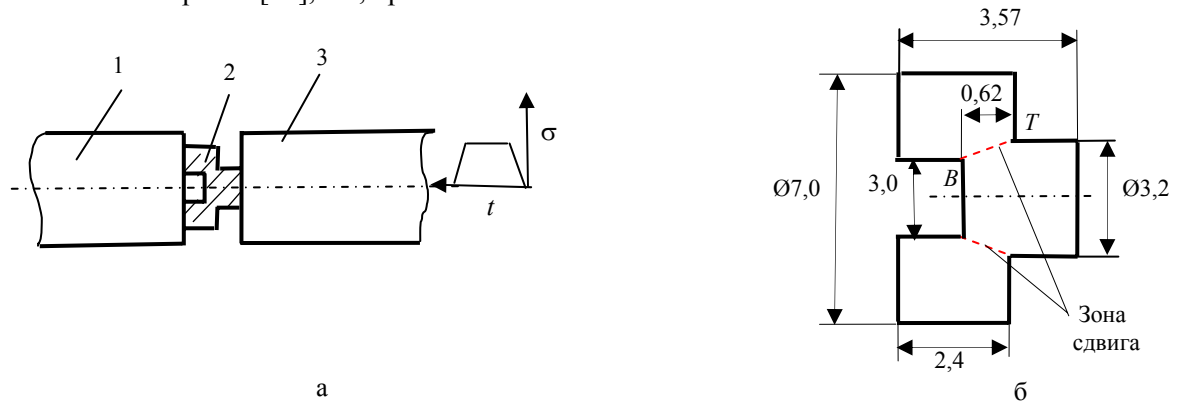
Схема проведения опытов (а) и геометрия образцов (б): а: 1 – опорный стержень, 2 – образец, 3 – нагружающий стержень
